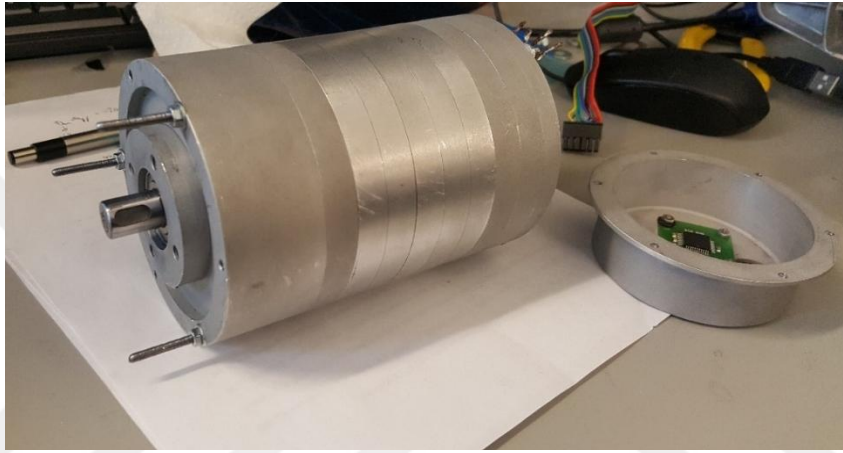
Yüksek hızlı ARM bileşenleri (stator, sargılar, gövde, rotor, şaft ve rulmanlar)
